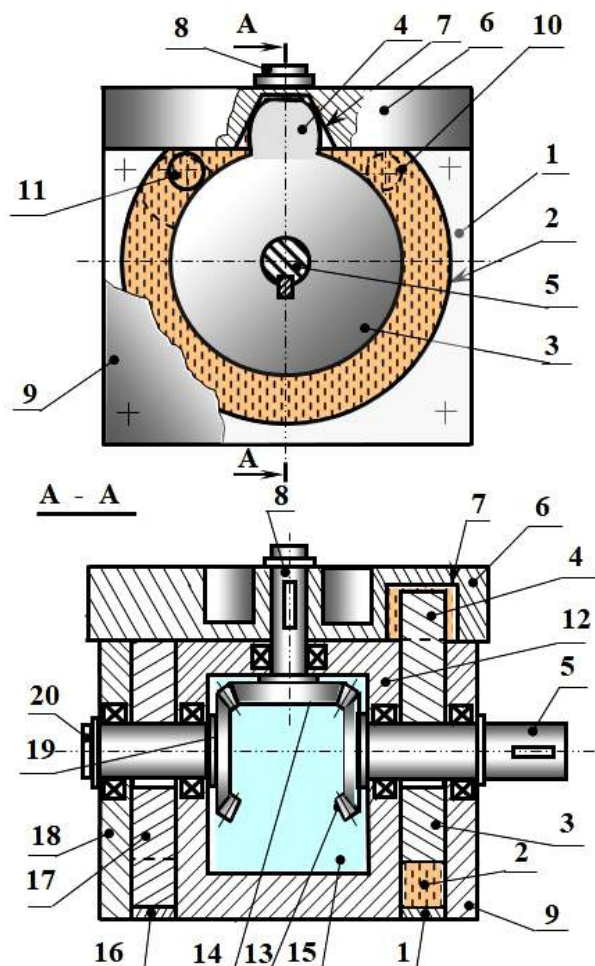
Схема прямозубого роторного насоса с двумя рабочими полостями: 1 — 1-й цилиндр; 2 — 1-я рабочая полость; 3 — 1-й ротор; 4 — зуб 1-го ротора; 5 — приводной вал; 6 — уплотнительный диск; 7 — впадина; 8 — промежуточный вал; 9 — крышка 1-го цилиндра; 10 — всасывающее окно; 11 — нагнетательный клапан; 12 — корпус; 13 — ведущая шестерня; 14 — промежуточная шестерня; 15 — полость корпуса; 16 — 2-й цилиндр; 17 — 2-й ротор; 18 — крышка; 19 — ведомая шестерня; 20 — ведомый вал
